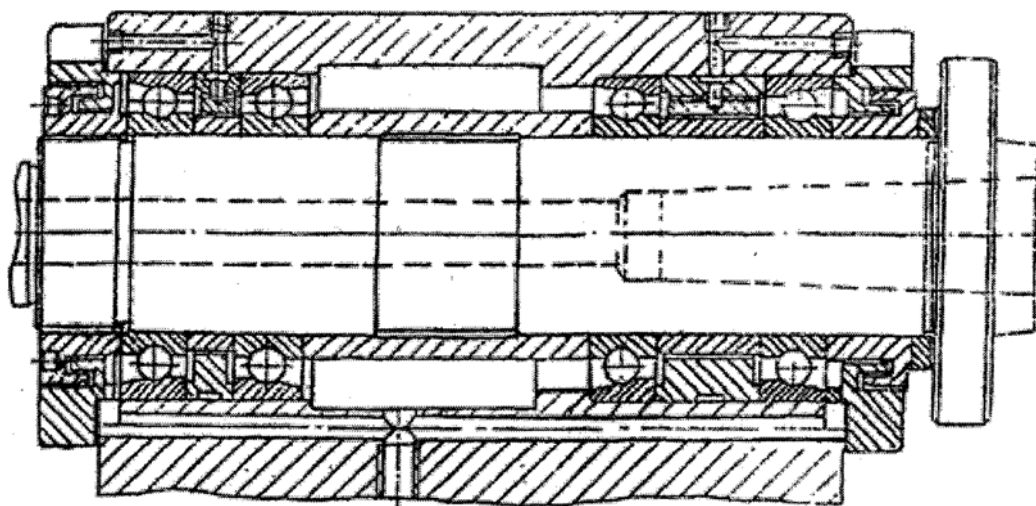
Шпиндельный узел станка на шариковых упорно-радиальных подшипниках типа 36000 или 46000, собранных в комплекте по два по схеме дуплекс 0-образной в двух опорах
